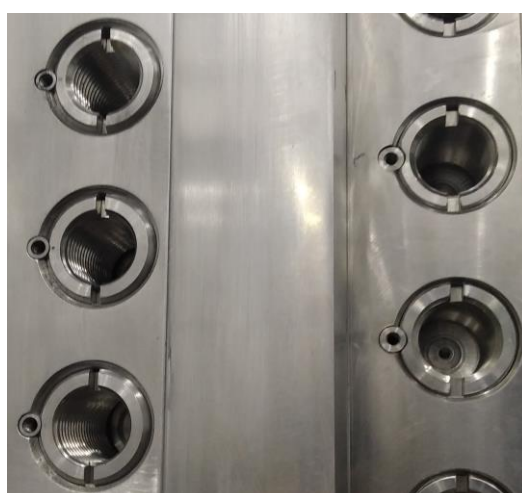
Типовая конструкция расположения элементов комбинированных резьбовых соединений
